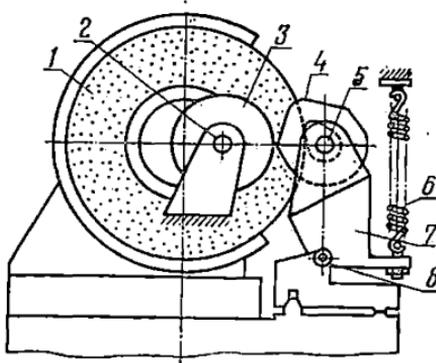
Схема станка для шлифования кулачков распределительного вала:
